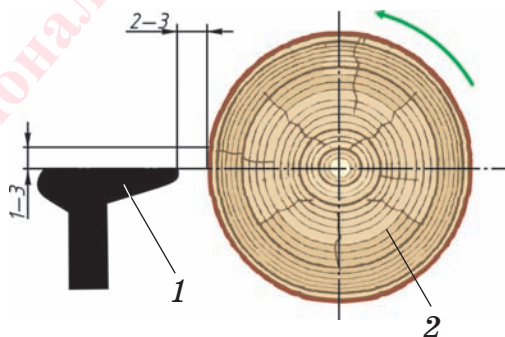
Расположение подручника (1) относительно заготовки (2)
